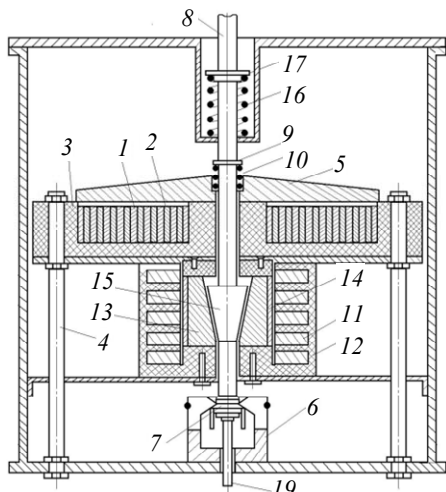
Короткозамыкатель с антидриблинговым устройством: 1 – многовитковый индуктор; 2 – эпоксидный компаунд; 3 – стеклотекстолитовая оправа; 4 – крепежные болты; 5 – диск ИДМ; 6 – защелка; 7 – конус штока; 8 – шток; 9 – кольцевой выступ; 10 – пружина; 11 – индуктор; 12 – изолированный корпус; 13 – втулка; 14 – медное покрытие; 15 – выступ штока; 16 – пружина; 17 – кольцевой выступ; 18 – биметаллическая пружина; 19 – тяга электромагнитов
